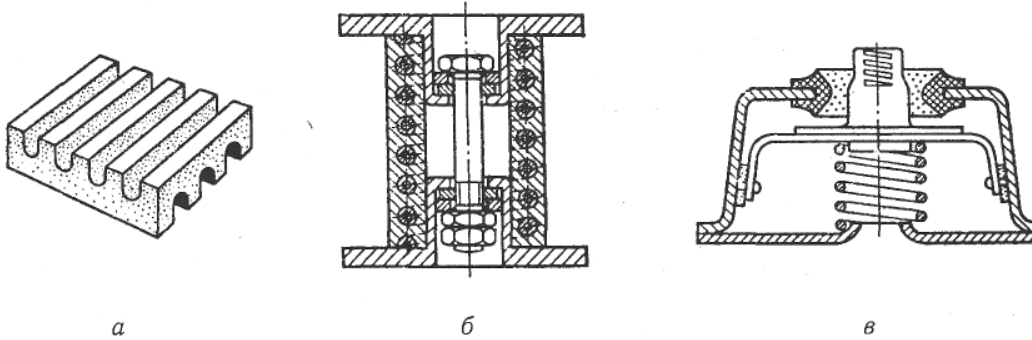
Віброізоляційні амортизатори: а — ребриста гума; б — пружинний амортизатор запресований у гумову масу; в — комбінований (пружинно-гумовий) амортизатор
